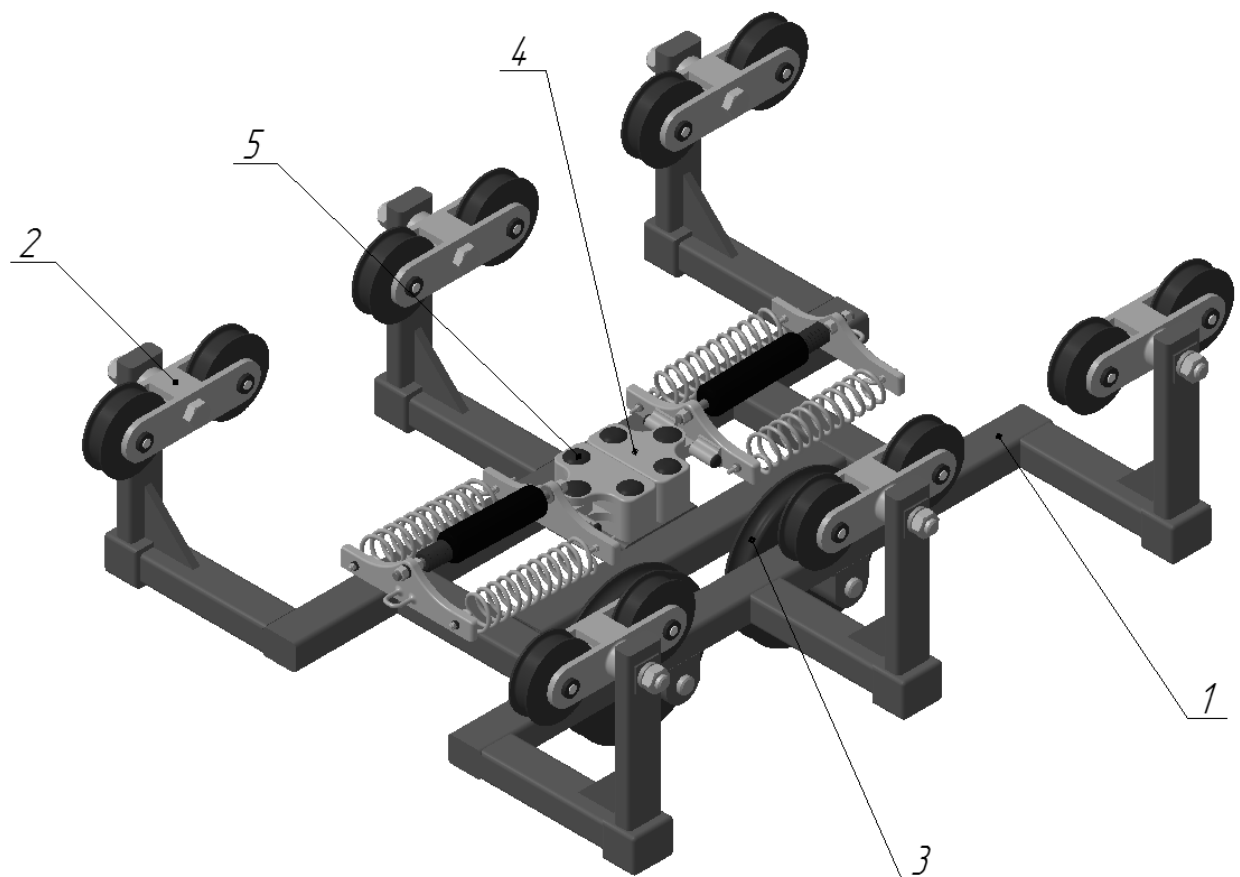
Загальний вигляд розробленої конструкції вантажного візка
